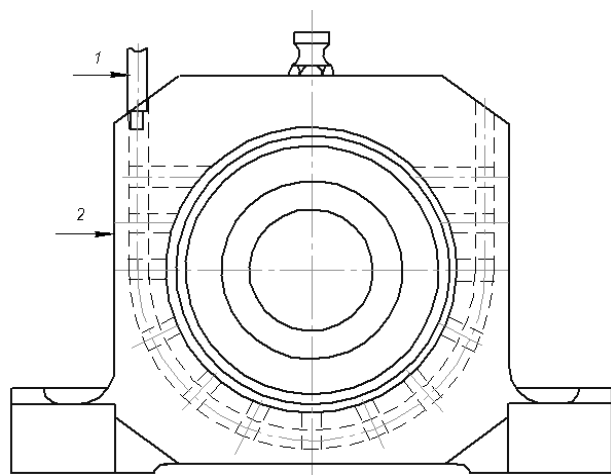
Получение отверстий в корпусе: 1 – инструмент электроэрозионного оборудования; 2 – корпус подшипника
